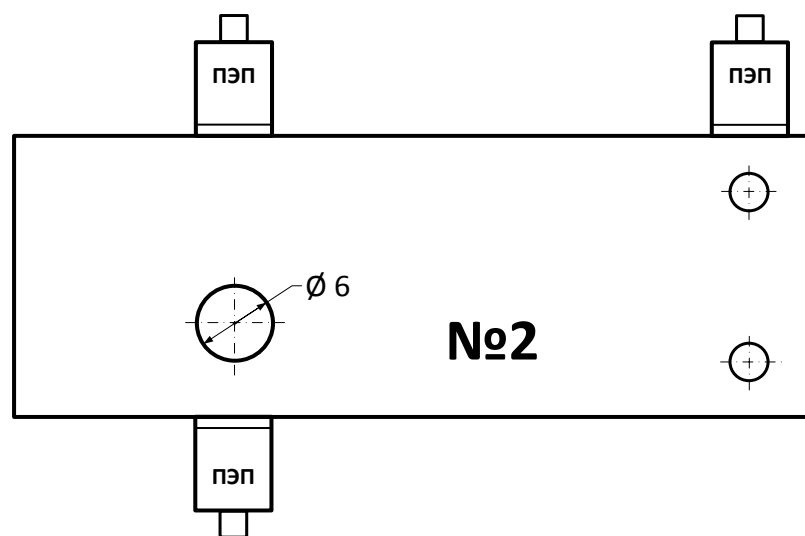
Установка ПЭП S3568 2.5A0D10CL на образце № 2 из комплекта КОУ-2
